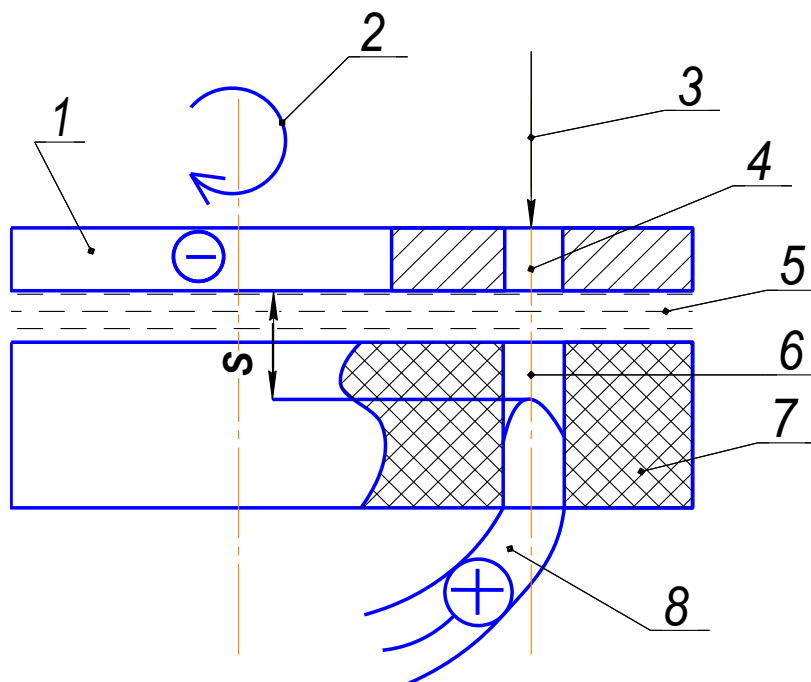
Схема получения отверстий большой глубины с наложением ультразвука:
